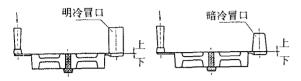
齿轮的冷边冒口工艺(湿型,内浇道2~4个) Fig.5 Method of a gear wheel with a side cold riser (green mold,2 or 4 ingates)
